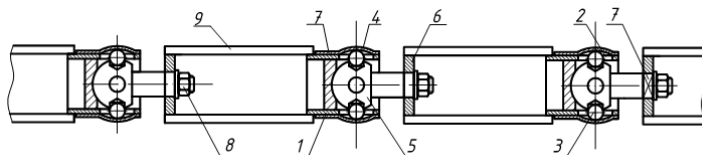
Конструктивна схема гвинтового секційного шарнірного робочого органу
